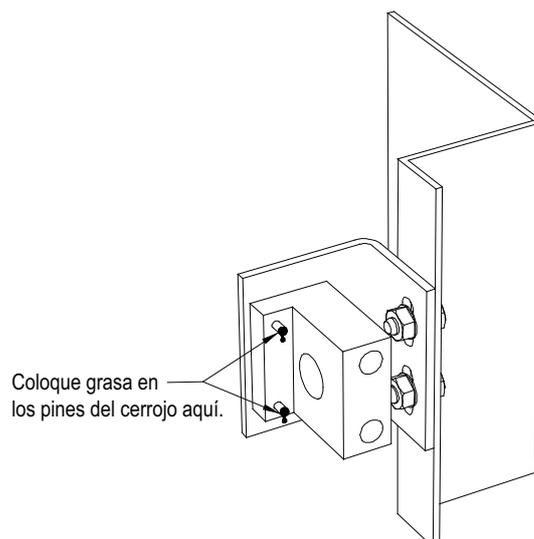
Pieza de encaje de cerradura montada en el gabinete
